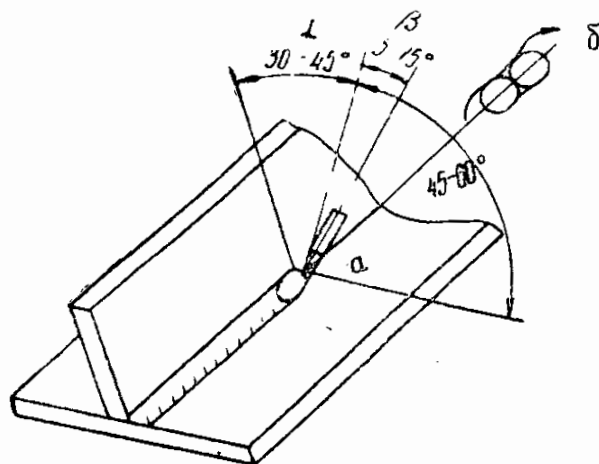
Положение (а) и схема перемещения (б) горелки (электрода) при полуавтоматической сварке угловых швов в углекислом газе.
